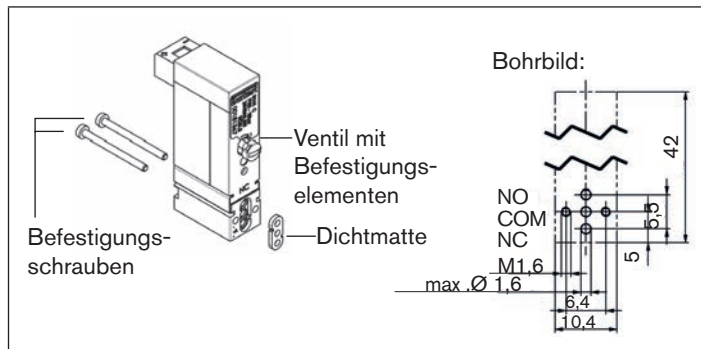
Montagezeichnung für Winkelflansch (FS09)
